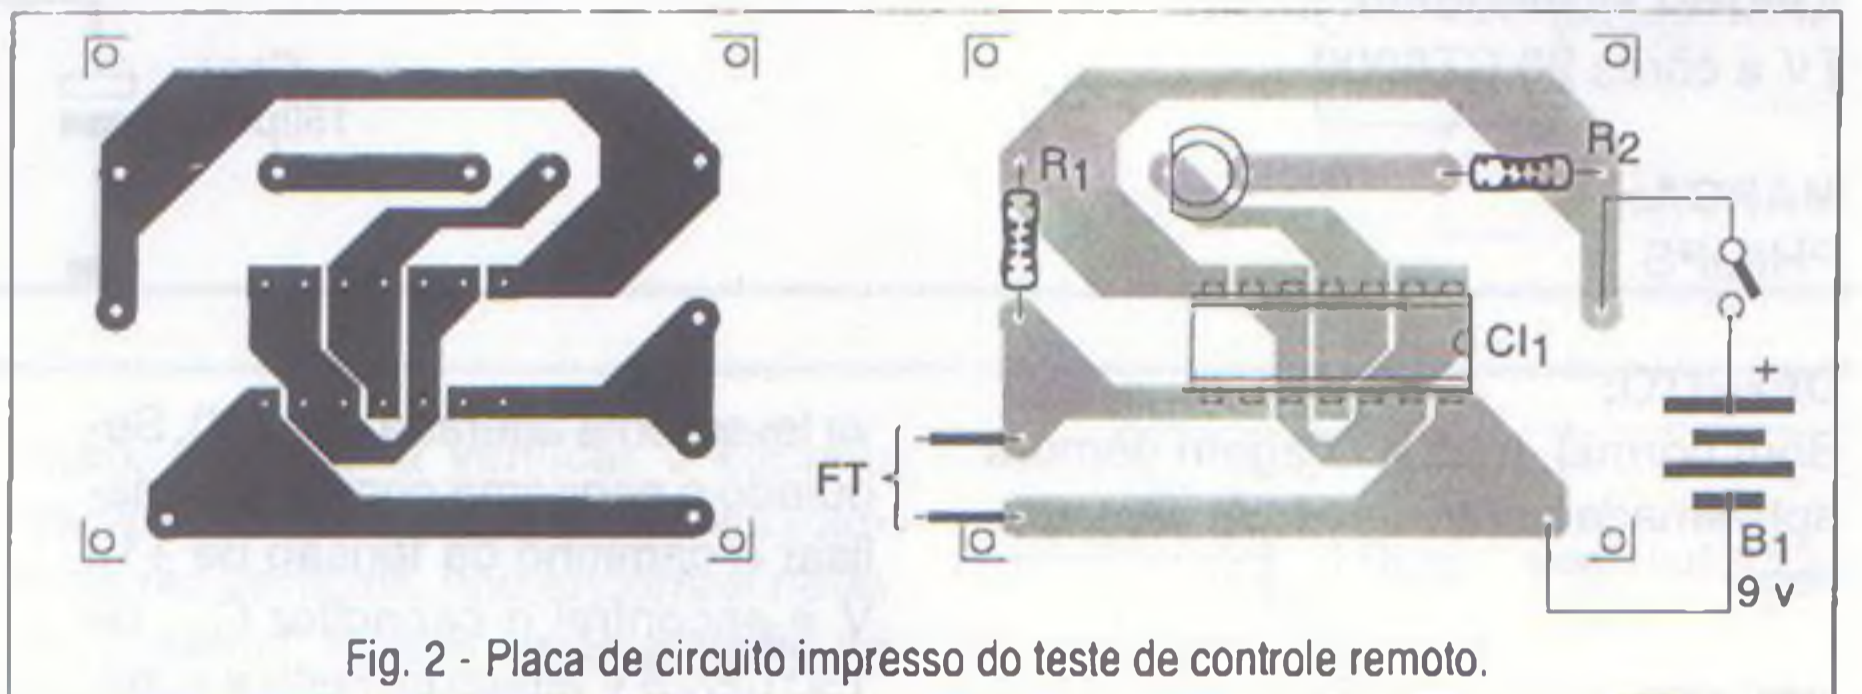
Placa de circuito impresso do teste de controle remoto.
